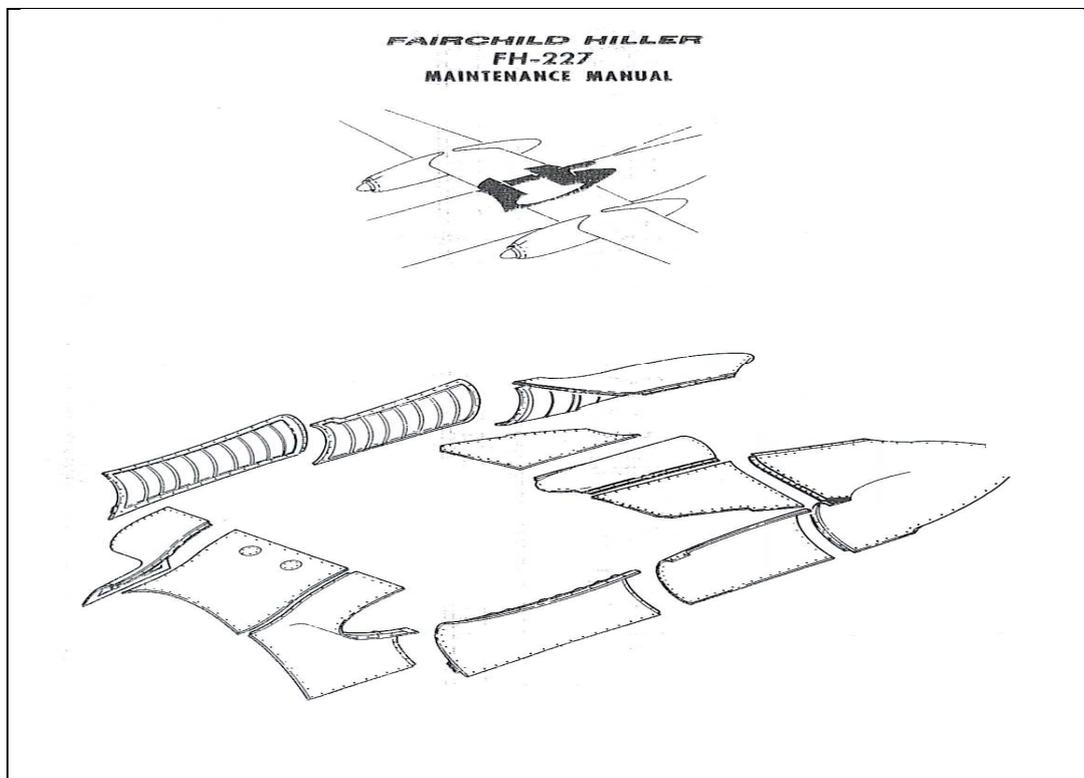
Wing Center Section to Fuselage Fairings
